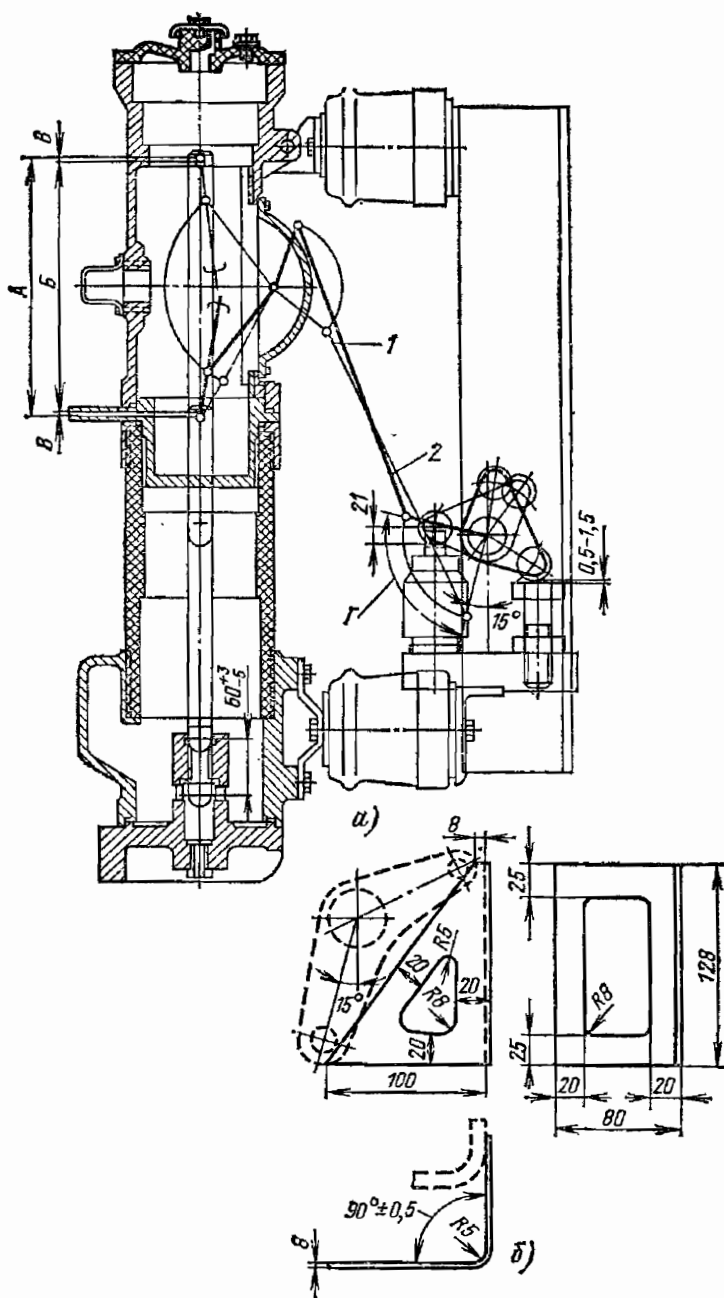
Регулировка приводного механизма выключателей типа ВМП-10:
